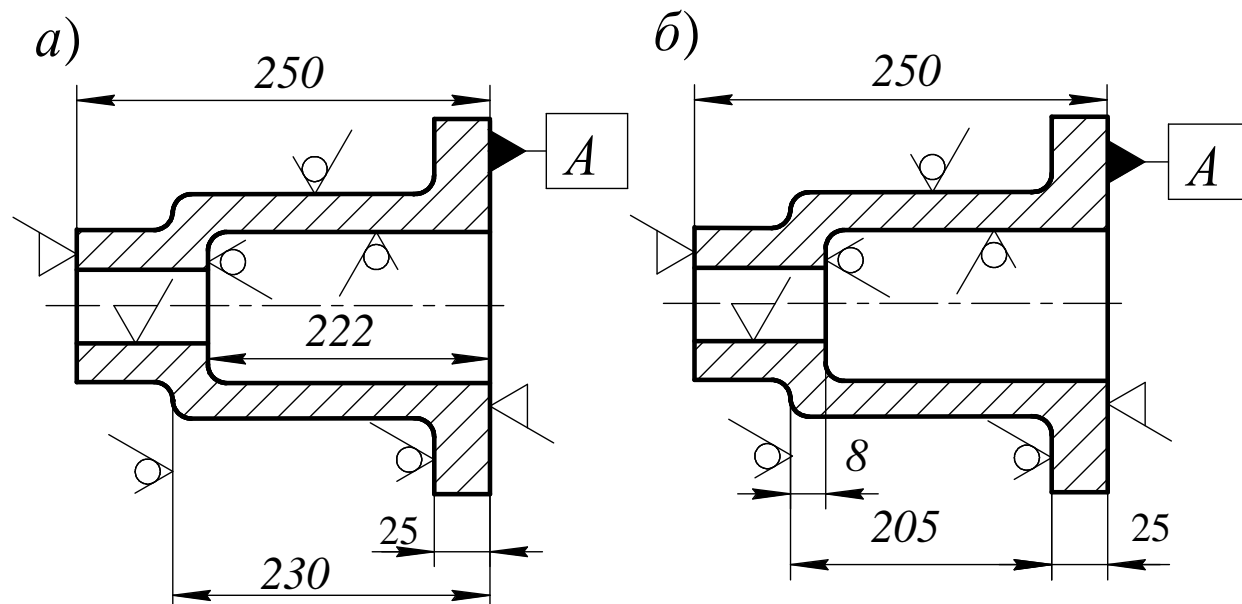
Схемы нанесения линейных размеров на чертеже детали, имеющей необрабатываемые методами резания поверхности:
